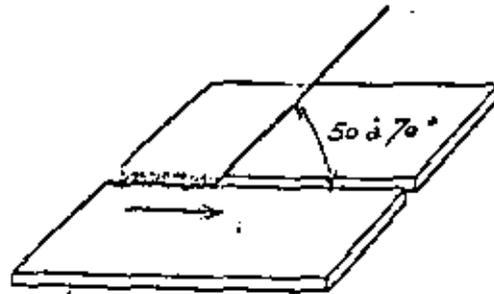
POSICION DEL ELECTRODO EN LA SOLDADURA HORIZONTAL.
